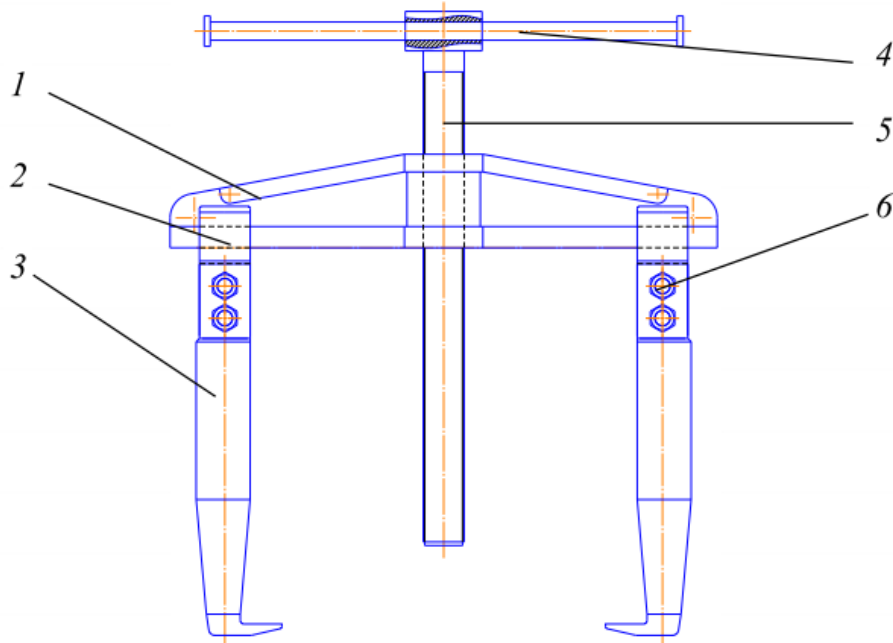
Загальний вигляд знімача: 1 – корпус-траверса; 2 – кронштейн; 3 – захоплювач опорний (важіль); 4 – вороток; 5 – силовий (упорний) гвинт; 6 – кріплення.
